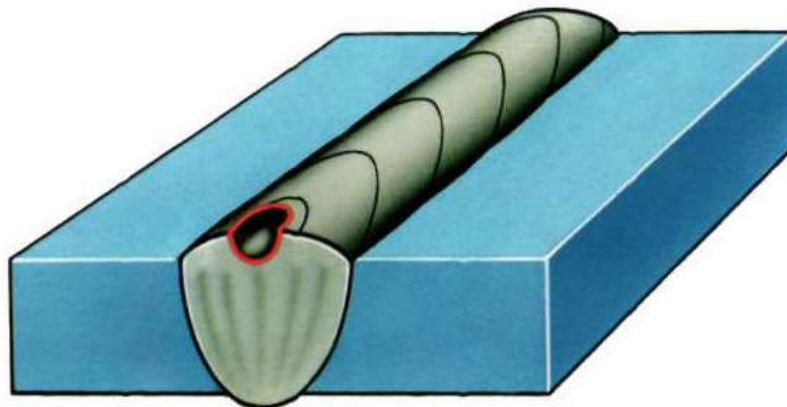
Дефекты сварного шва по типу поверхностной поры
